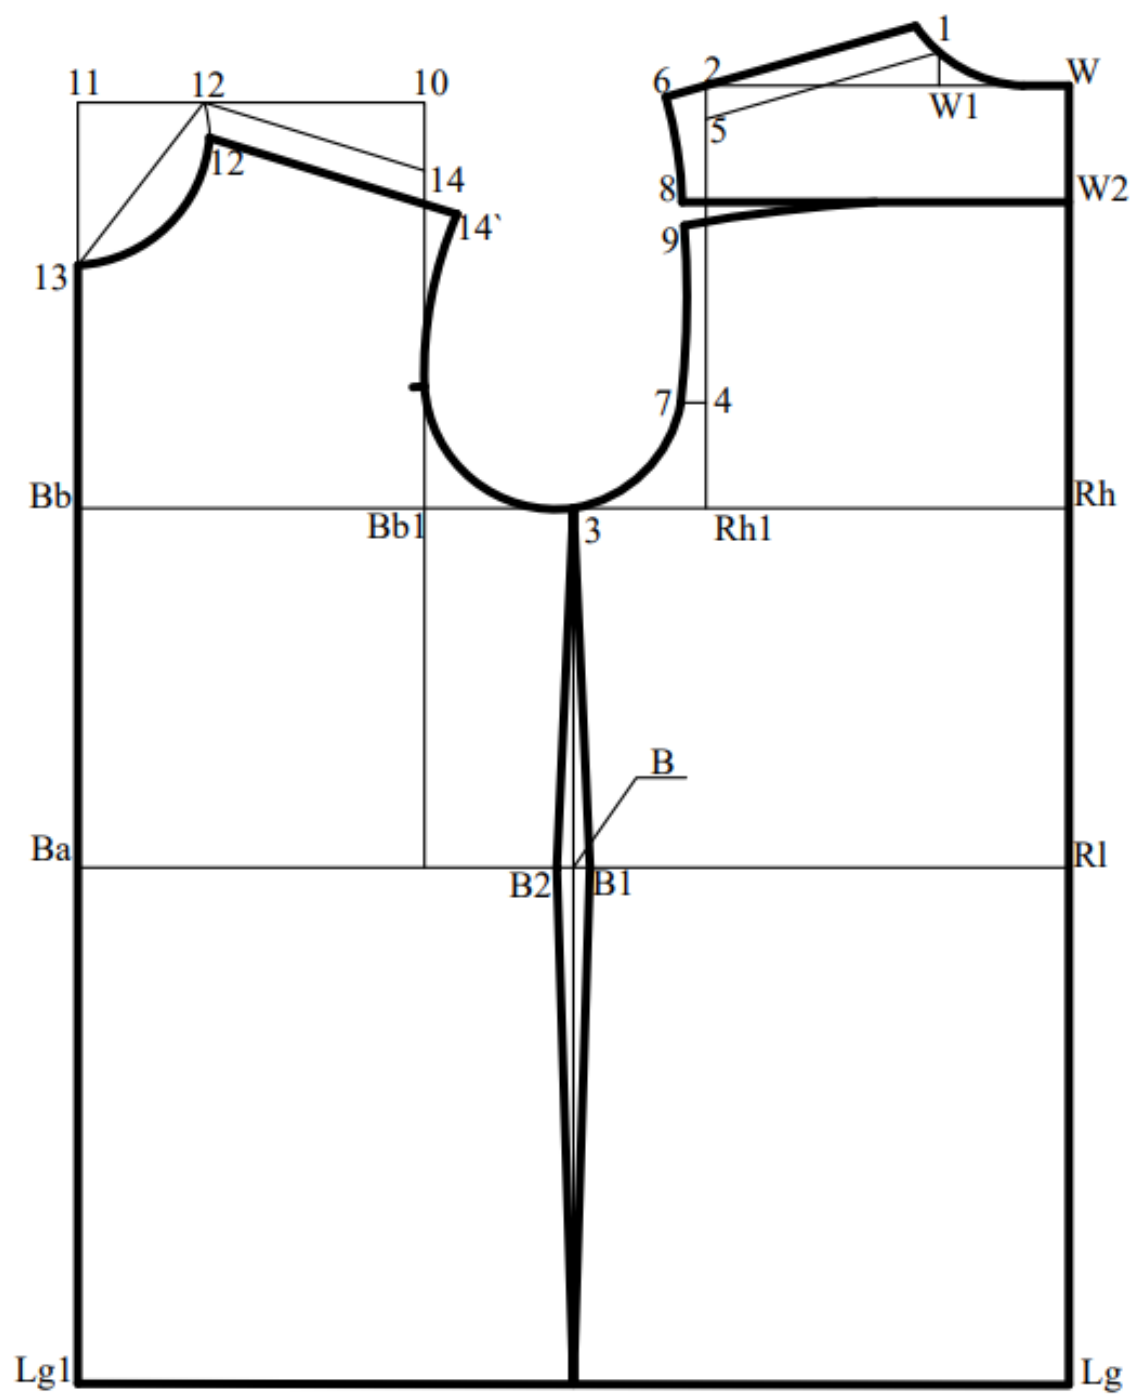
Чертёж базовой и исходной модельной конструкции спинки и переда мужской сорочки
